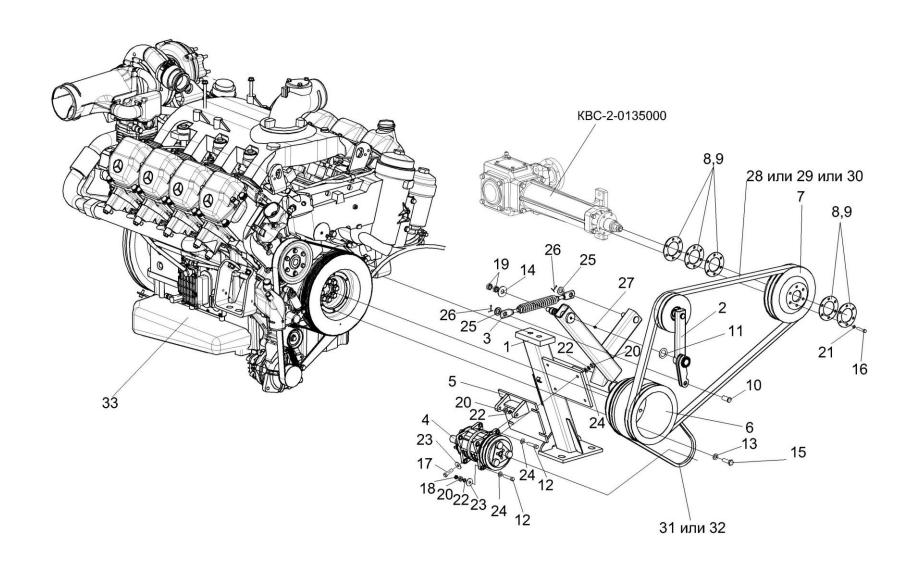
Установка двигателя OM502LA КВК 0150000 (установка ременных приводов)
